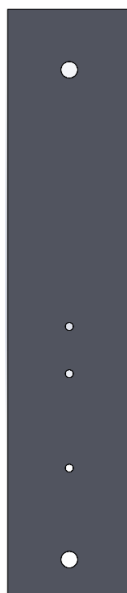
Стойка фронтального сварочного контура
